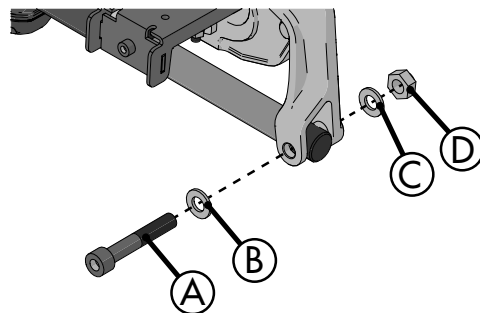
Hintere Befestigung der Stellvorrichtung.
